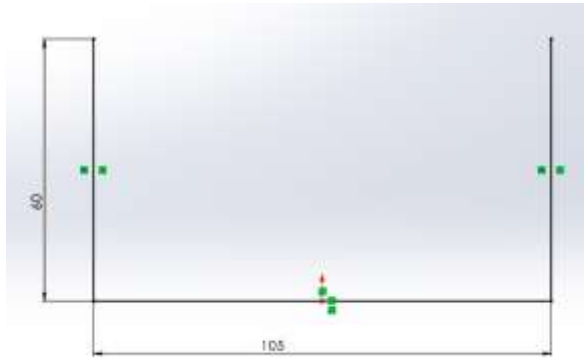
Створення базового ескізу деталі «Підставка»
